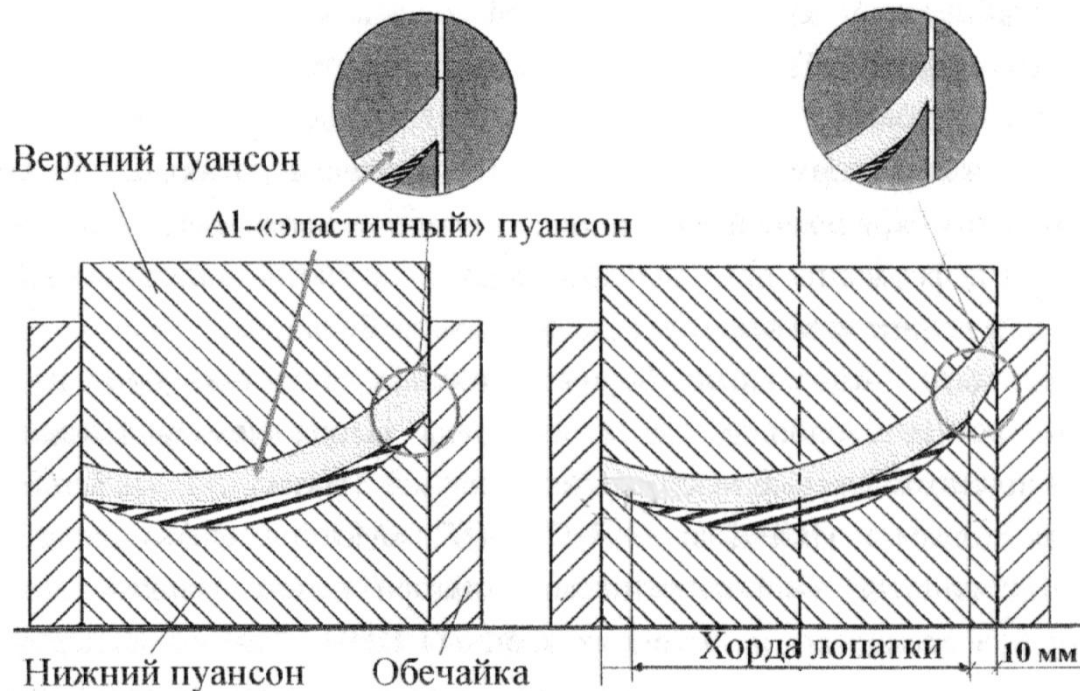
Схема сборки пакетной заготовки и горячее прессование при изготовлении турбинной лопатки
